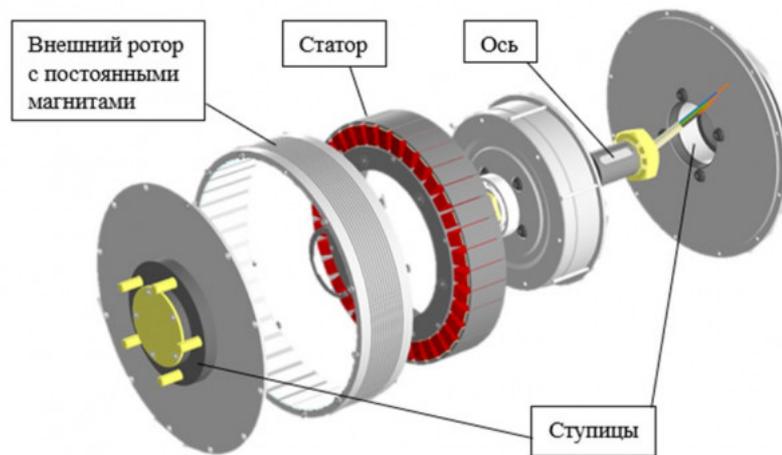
Сборочные единицы и детали мотора [Тишкевич: 361]
